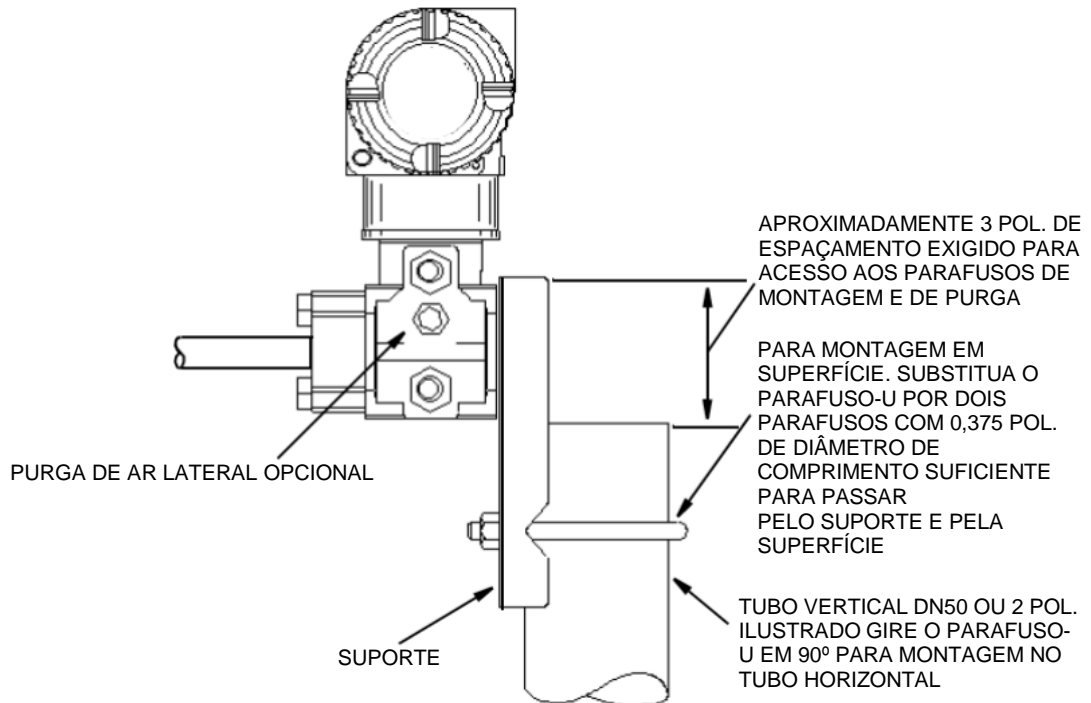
Montagem dos Transmissores IAP20 e IGP20
